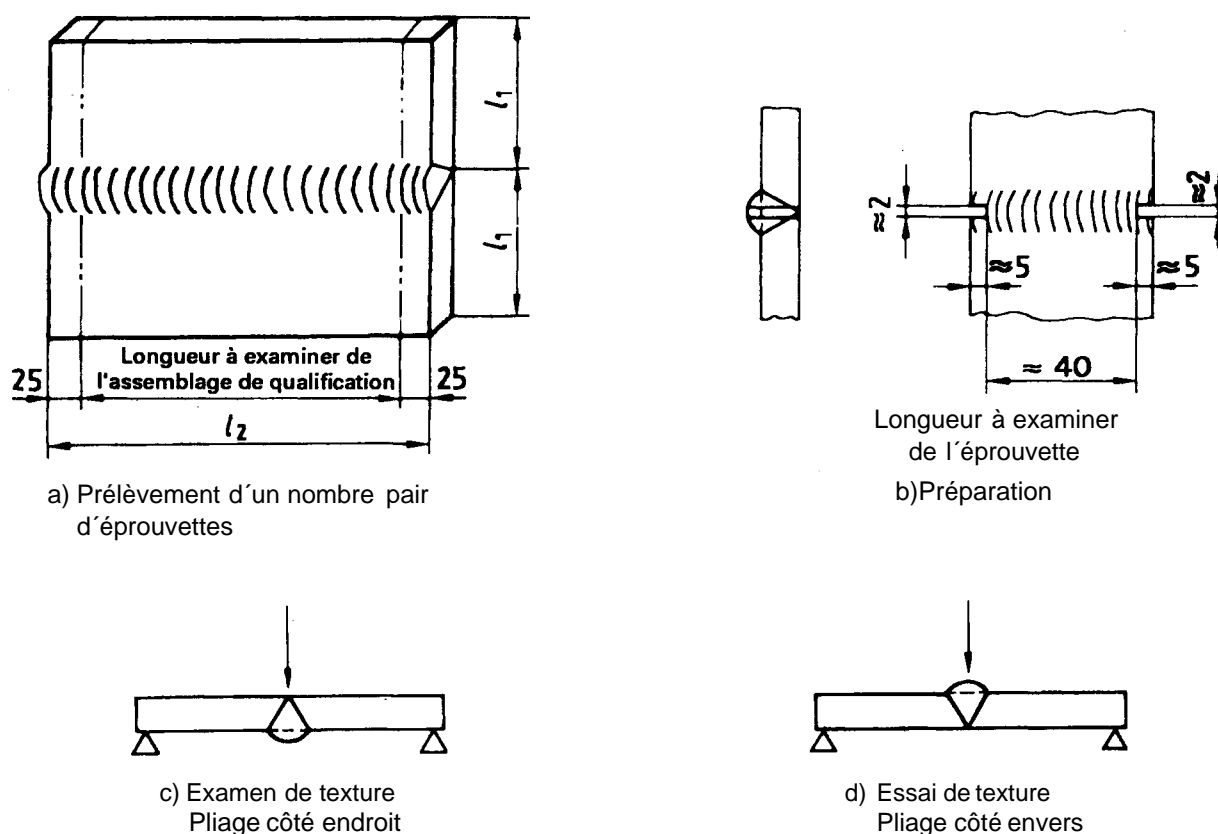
Préparation et essai des éprouvettes de texture d'assemblage de qualification bout à bout de tôles (Dimensions en mm)
